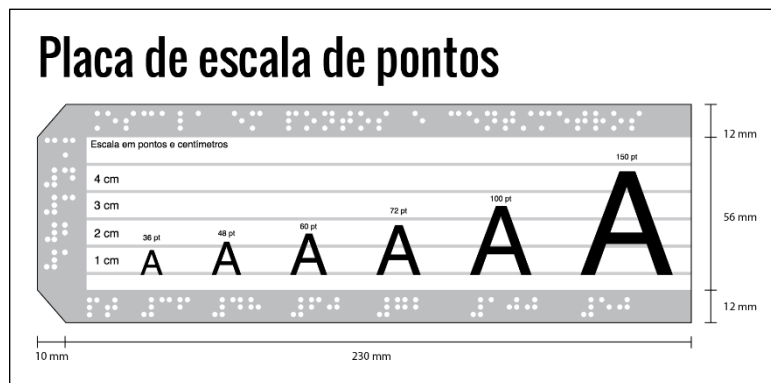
Desenho técnico da placa de escala de pontos (fonte: a autora)
